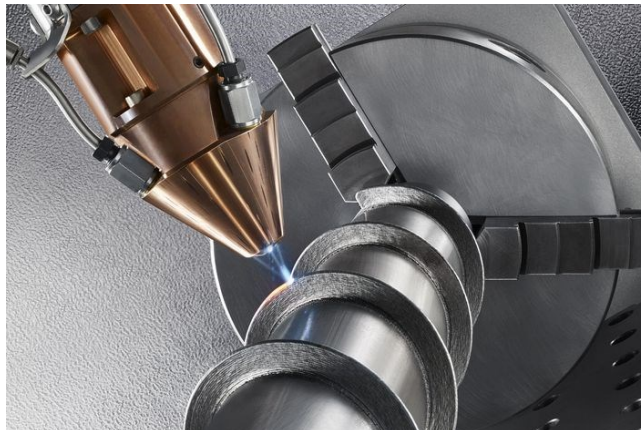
Základní princip metody Laser Metal Deposition [10]
